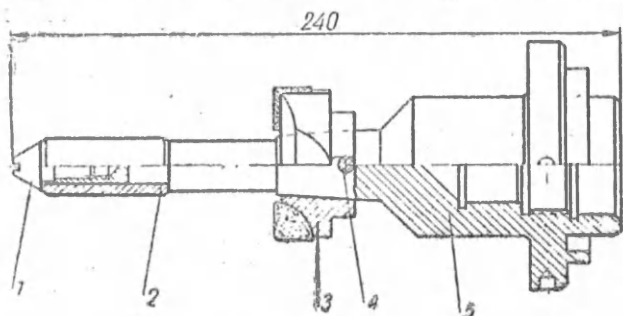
Оправка в сборе к станку 278Н для расточки клапанных гнезд головки цилиндров под кольца:
